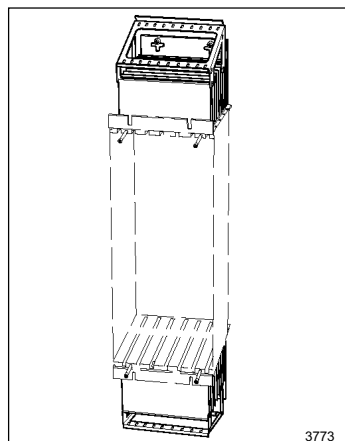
Кронштейны для установки АММ 4U на стене
